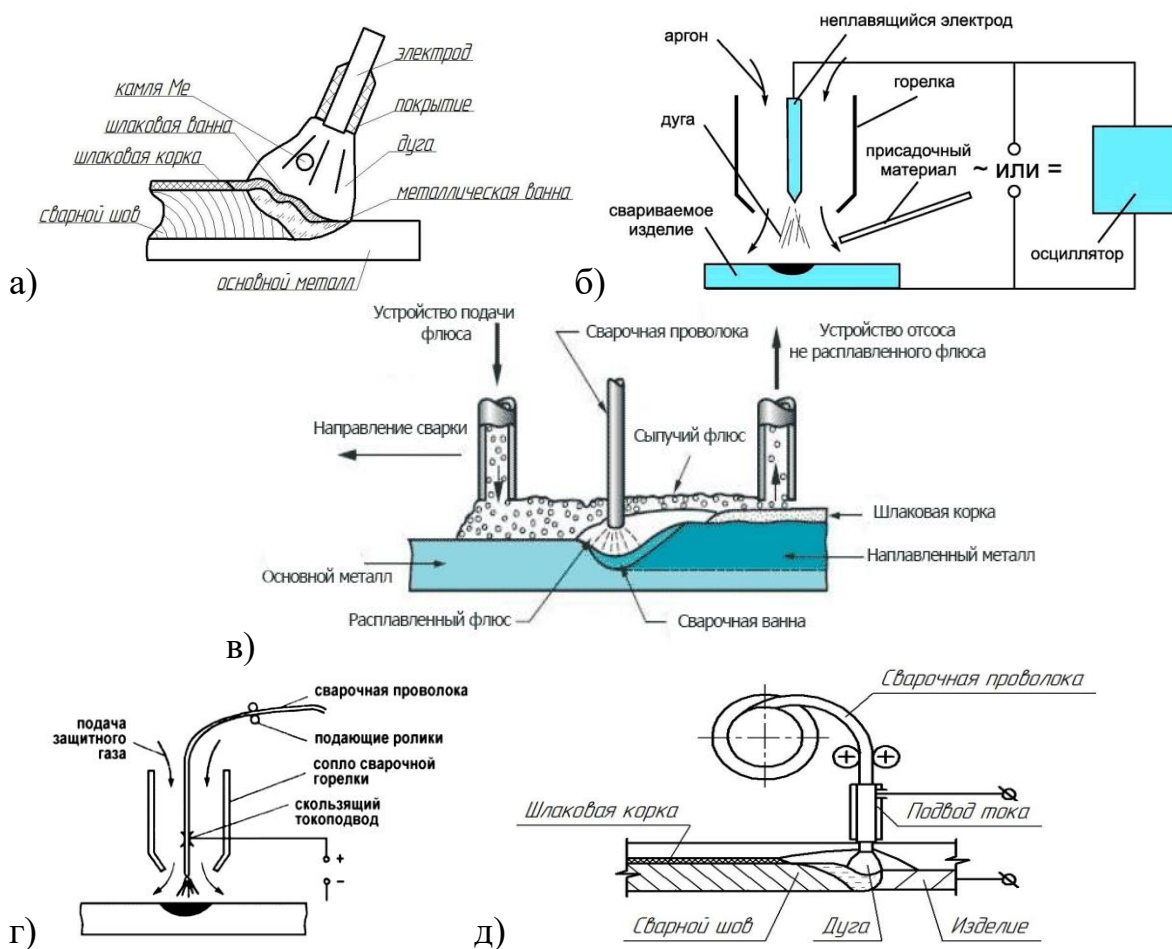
Рассматриваемые способы сварки: ручная дуговая (а), аргодуговая (б), под флюсом (в), механизированная в защитных газах (г), самозащитной проволокой (д)
